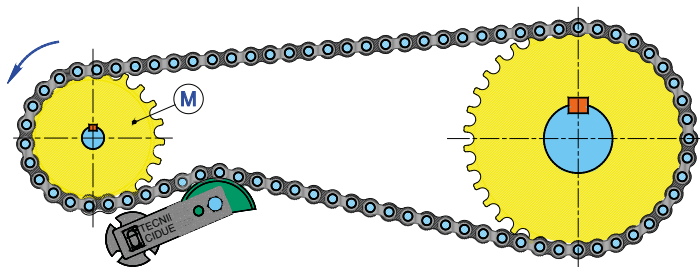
Montaggio CORRETTO (CONSIGLIATO!)
